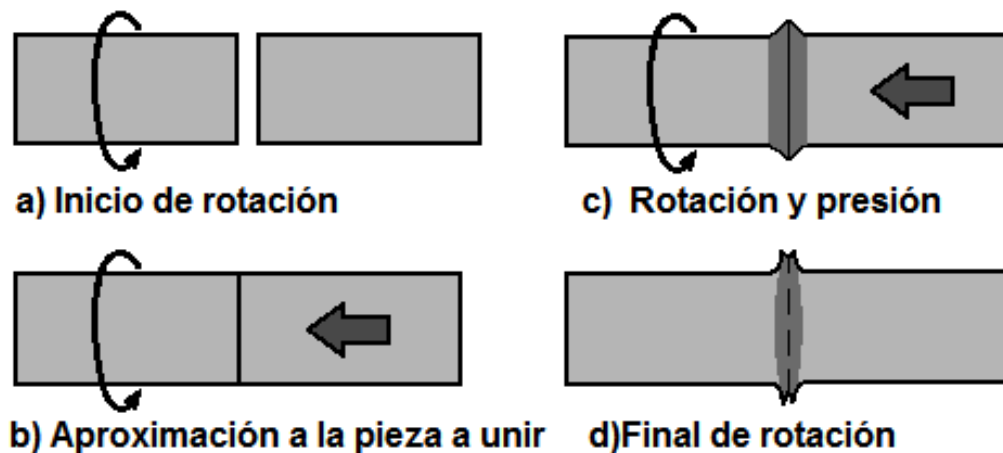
Esquema del proceso de soldadura por fricción (8, 18)
